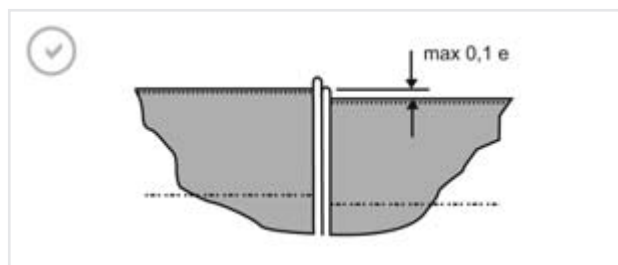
Soudure bout-à-bout avec désaxage des parois
